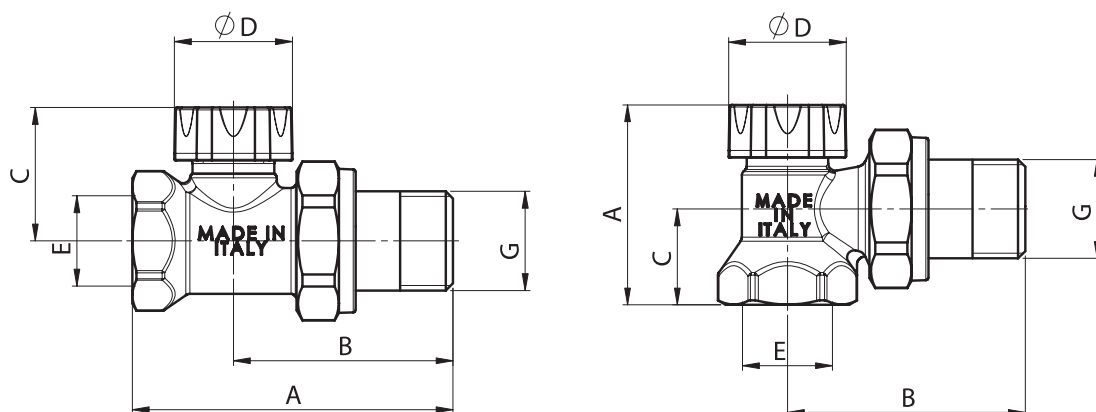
Габаритные и присоединительные размеры запорно-балансировочных клапанов типа SVL
